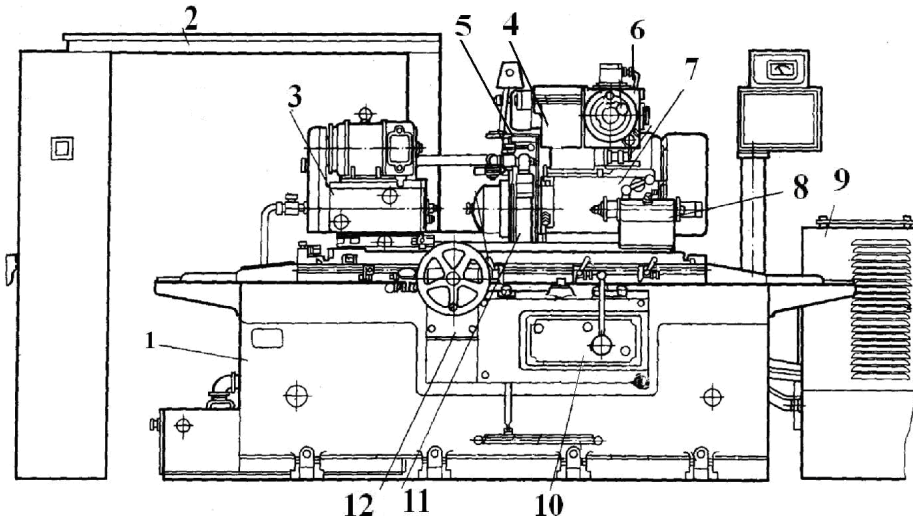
Загальний вигляд круглошліфувального верстата: 1 – станина; 2 – електрообігрівач; 3 – передня бабка; 4 – пристрій для внутрішнього шліфування; 5 – кожух шліфувального круга; 6 – механізм подач шліфувальної бабки; 7 – шліфувальна бабка; 8 – задня бабка; 9 – система гідроприводу та змащування; 10 – система гідроправління; 11 - шліфувальний круг; 12 – механізм ручного пересування столу.
